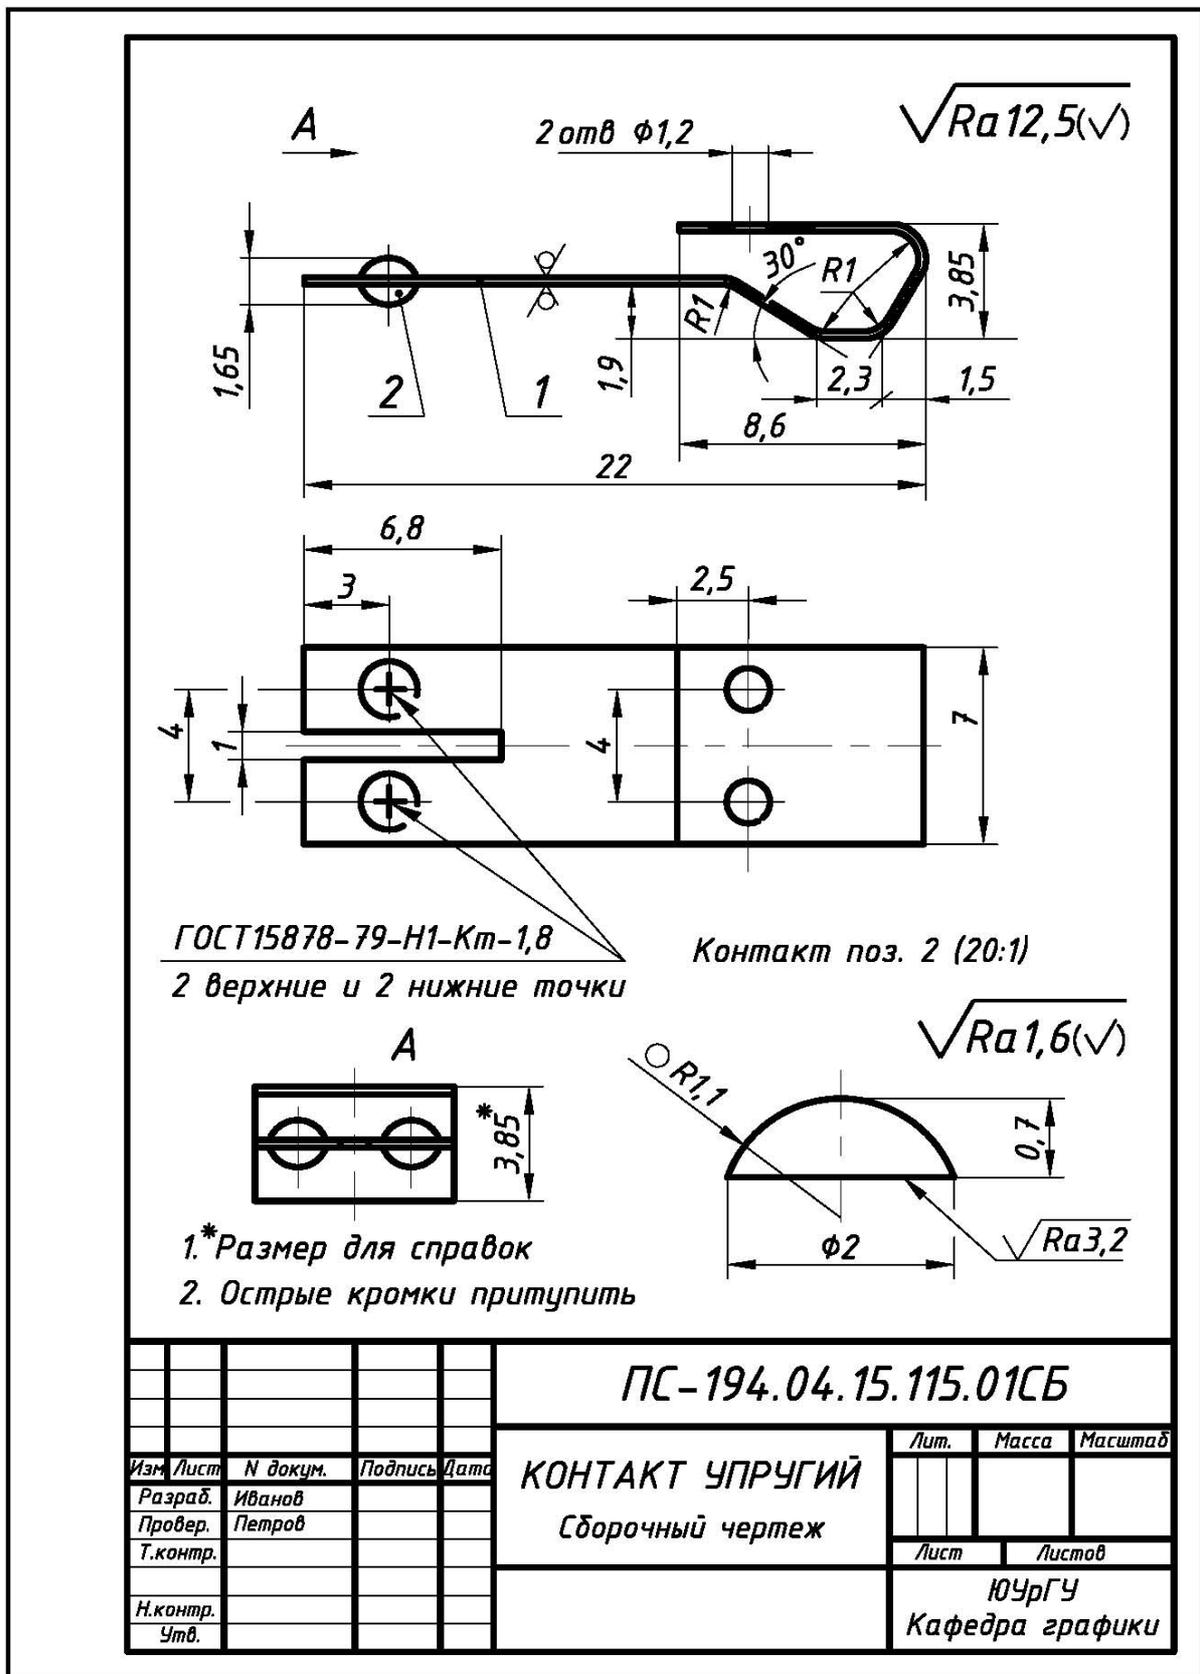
Пример выполнения и оформления эскиза единицы сборочной первого типа «Контакт упругий», образованной с помощью сборочной операции «Сварка точечная контактная»
